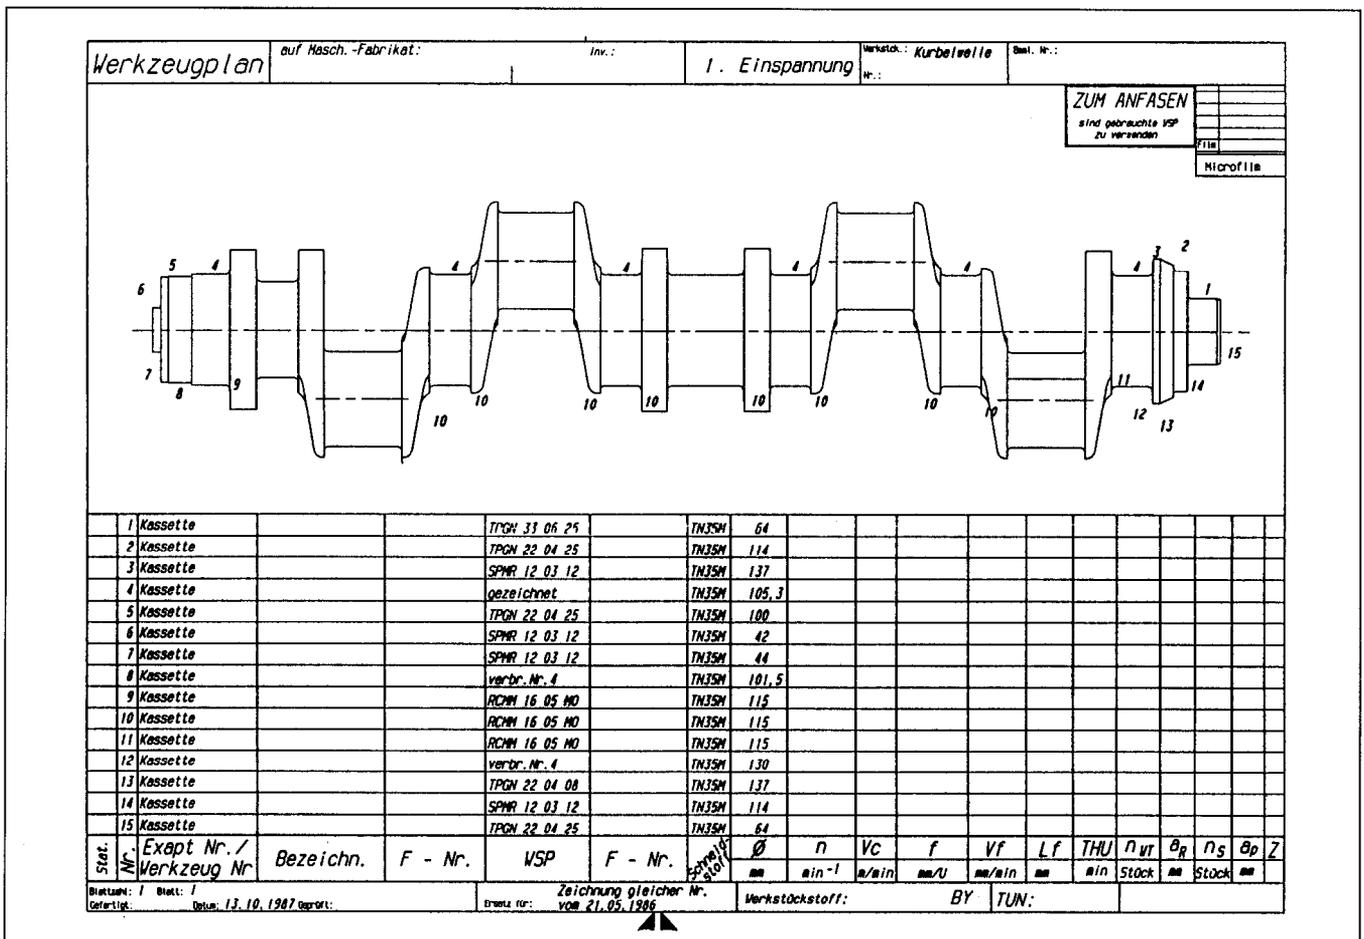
Werkzeugplan Kurbelwellenbearbeitung
